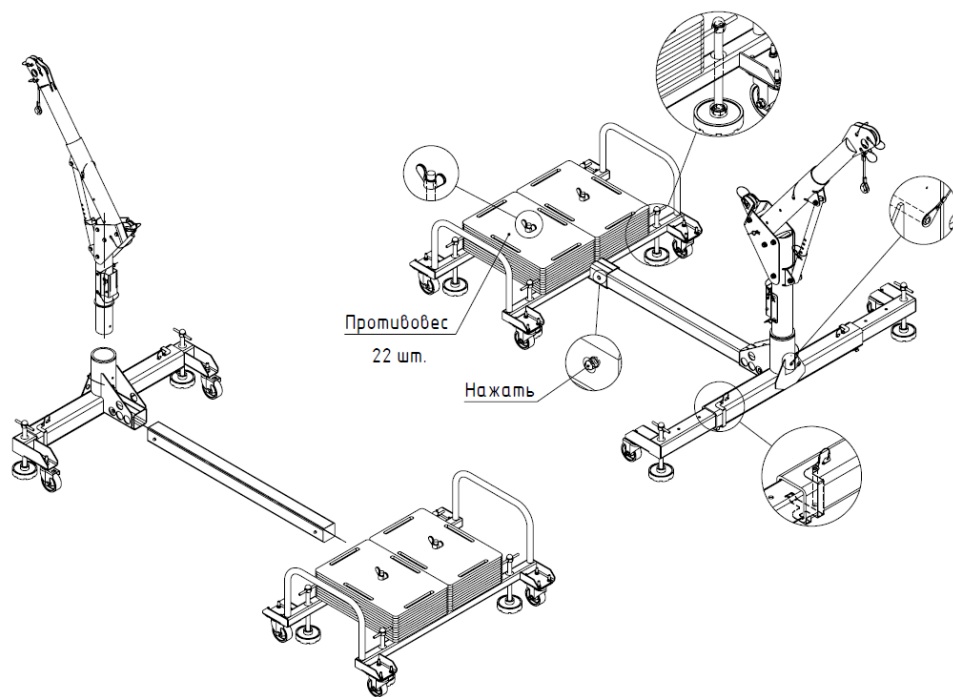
Монтаж СОБ Кран Е11-4L
